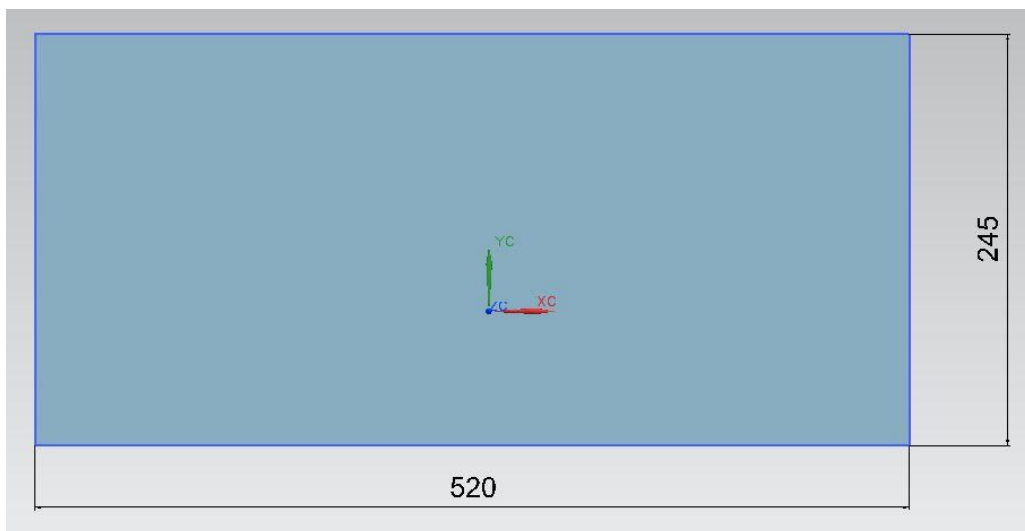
Конечный вид заготовки, полученный аналитическим методом
